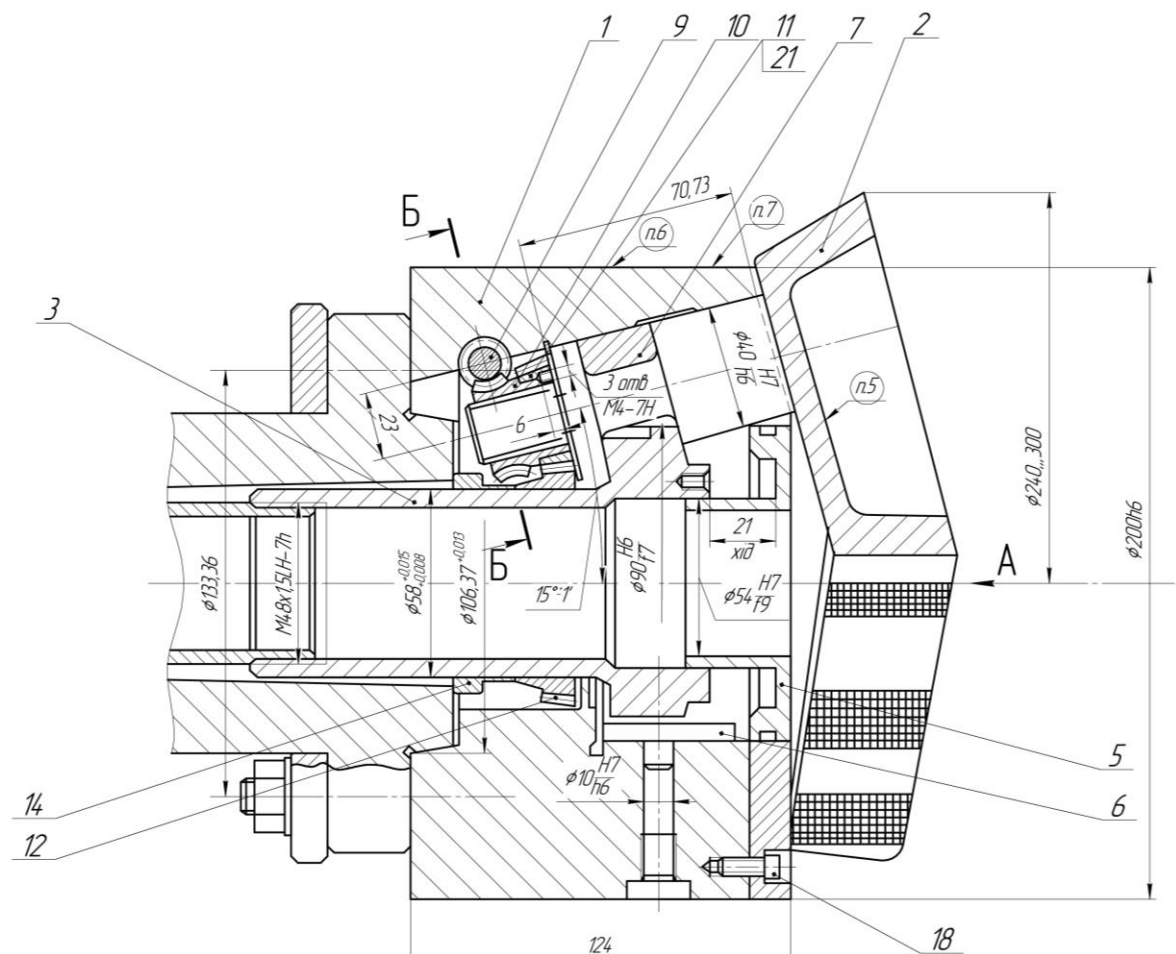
Конструкція затискного патрона плунжерного типу із поворотними призматичними кулачками для оснащення токарного верстата з ЧПК
